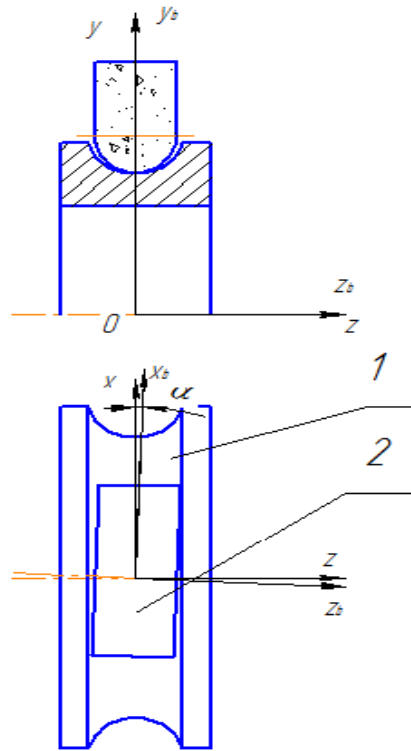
Схема расположения заготовки – 1 и абразивного бруска – 2 в процессе суперфиниширования
